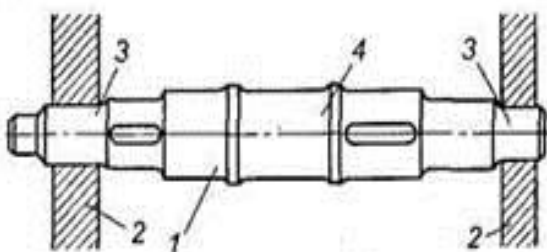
Прямой вал: 1 — вал; 2 — опоры вала; 3 — цапфы; 4 — шейка
